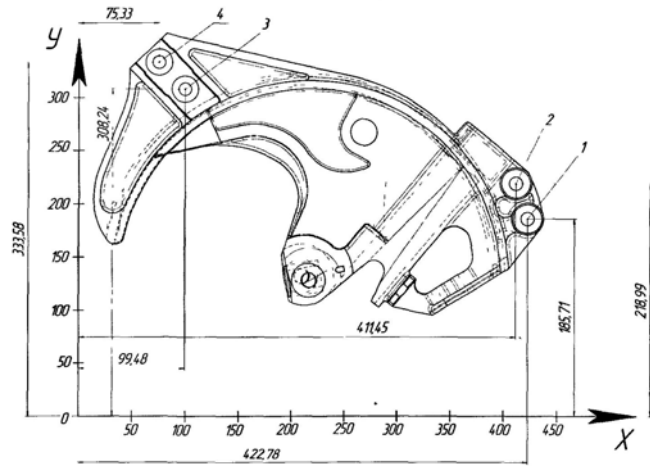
Деталь корпус у координатній площині для механічної обробки роботом
